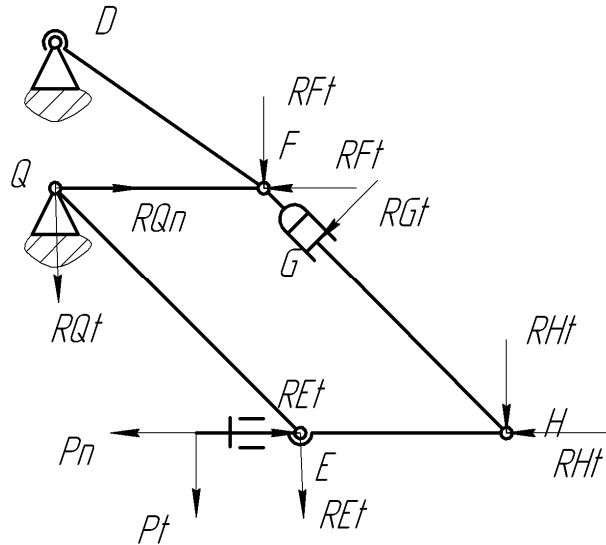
Схема для динамічного розрахунку механізму притискання колеса
